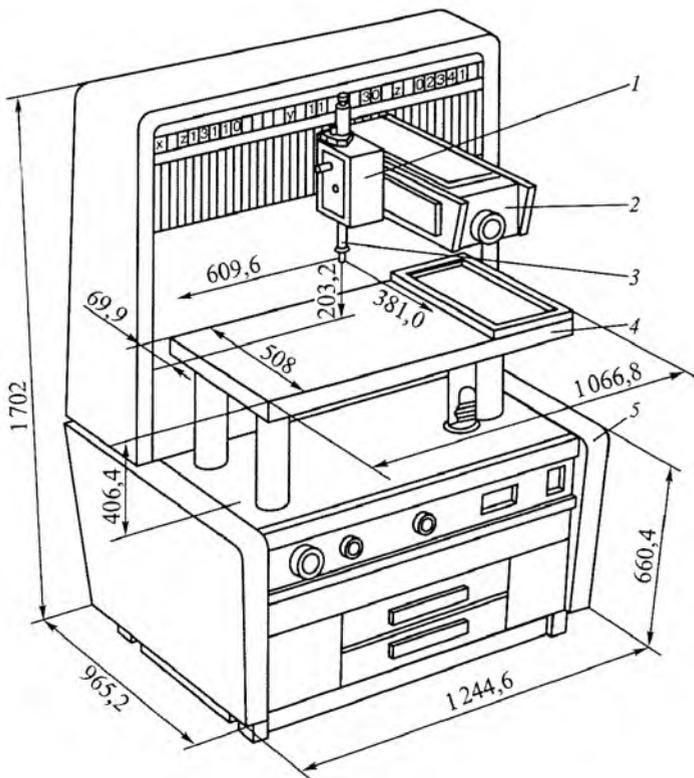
Координатно-разметочная машина для малогабаритных деталей (все размеры указаны в миллиметрах):
